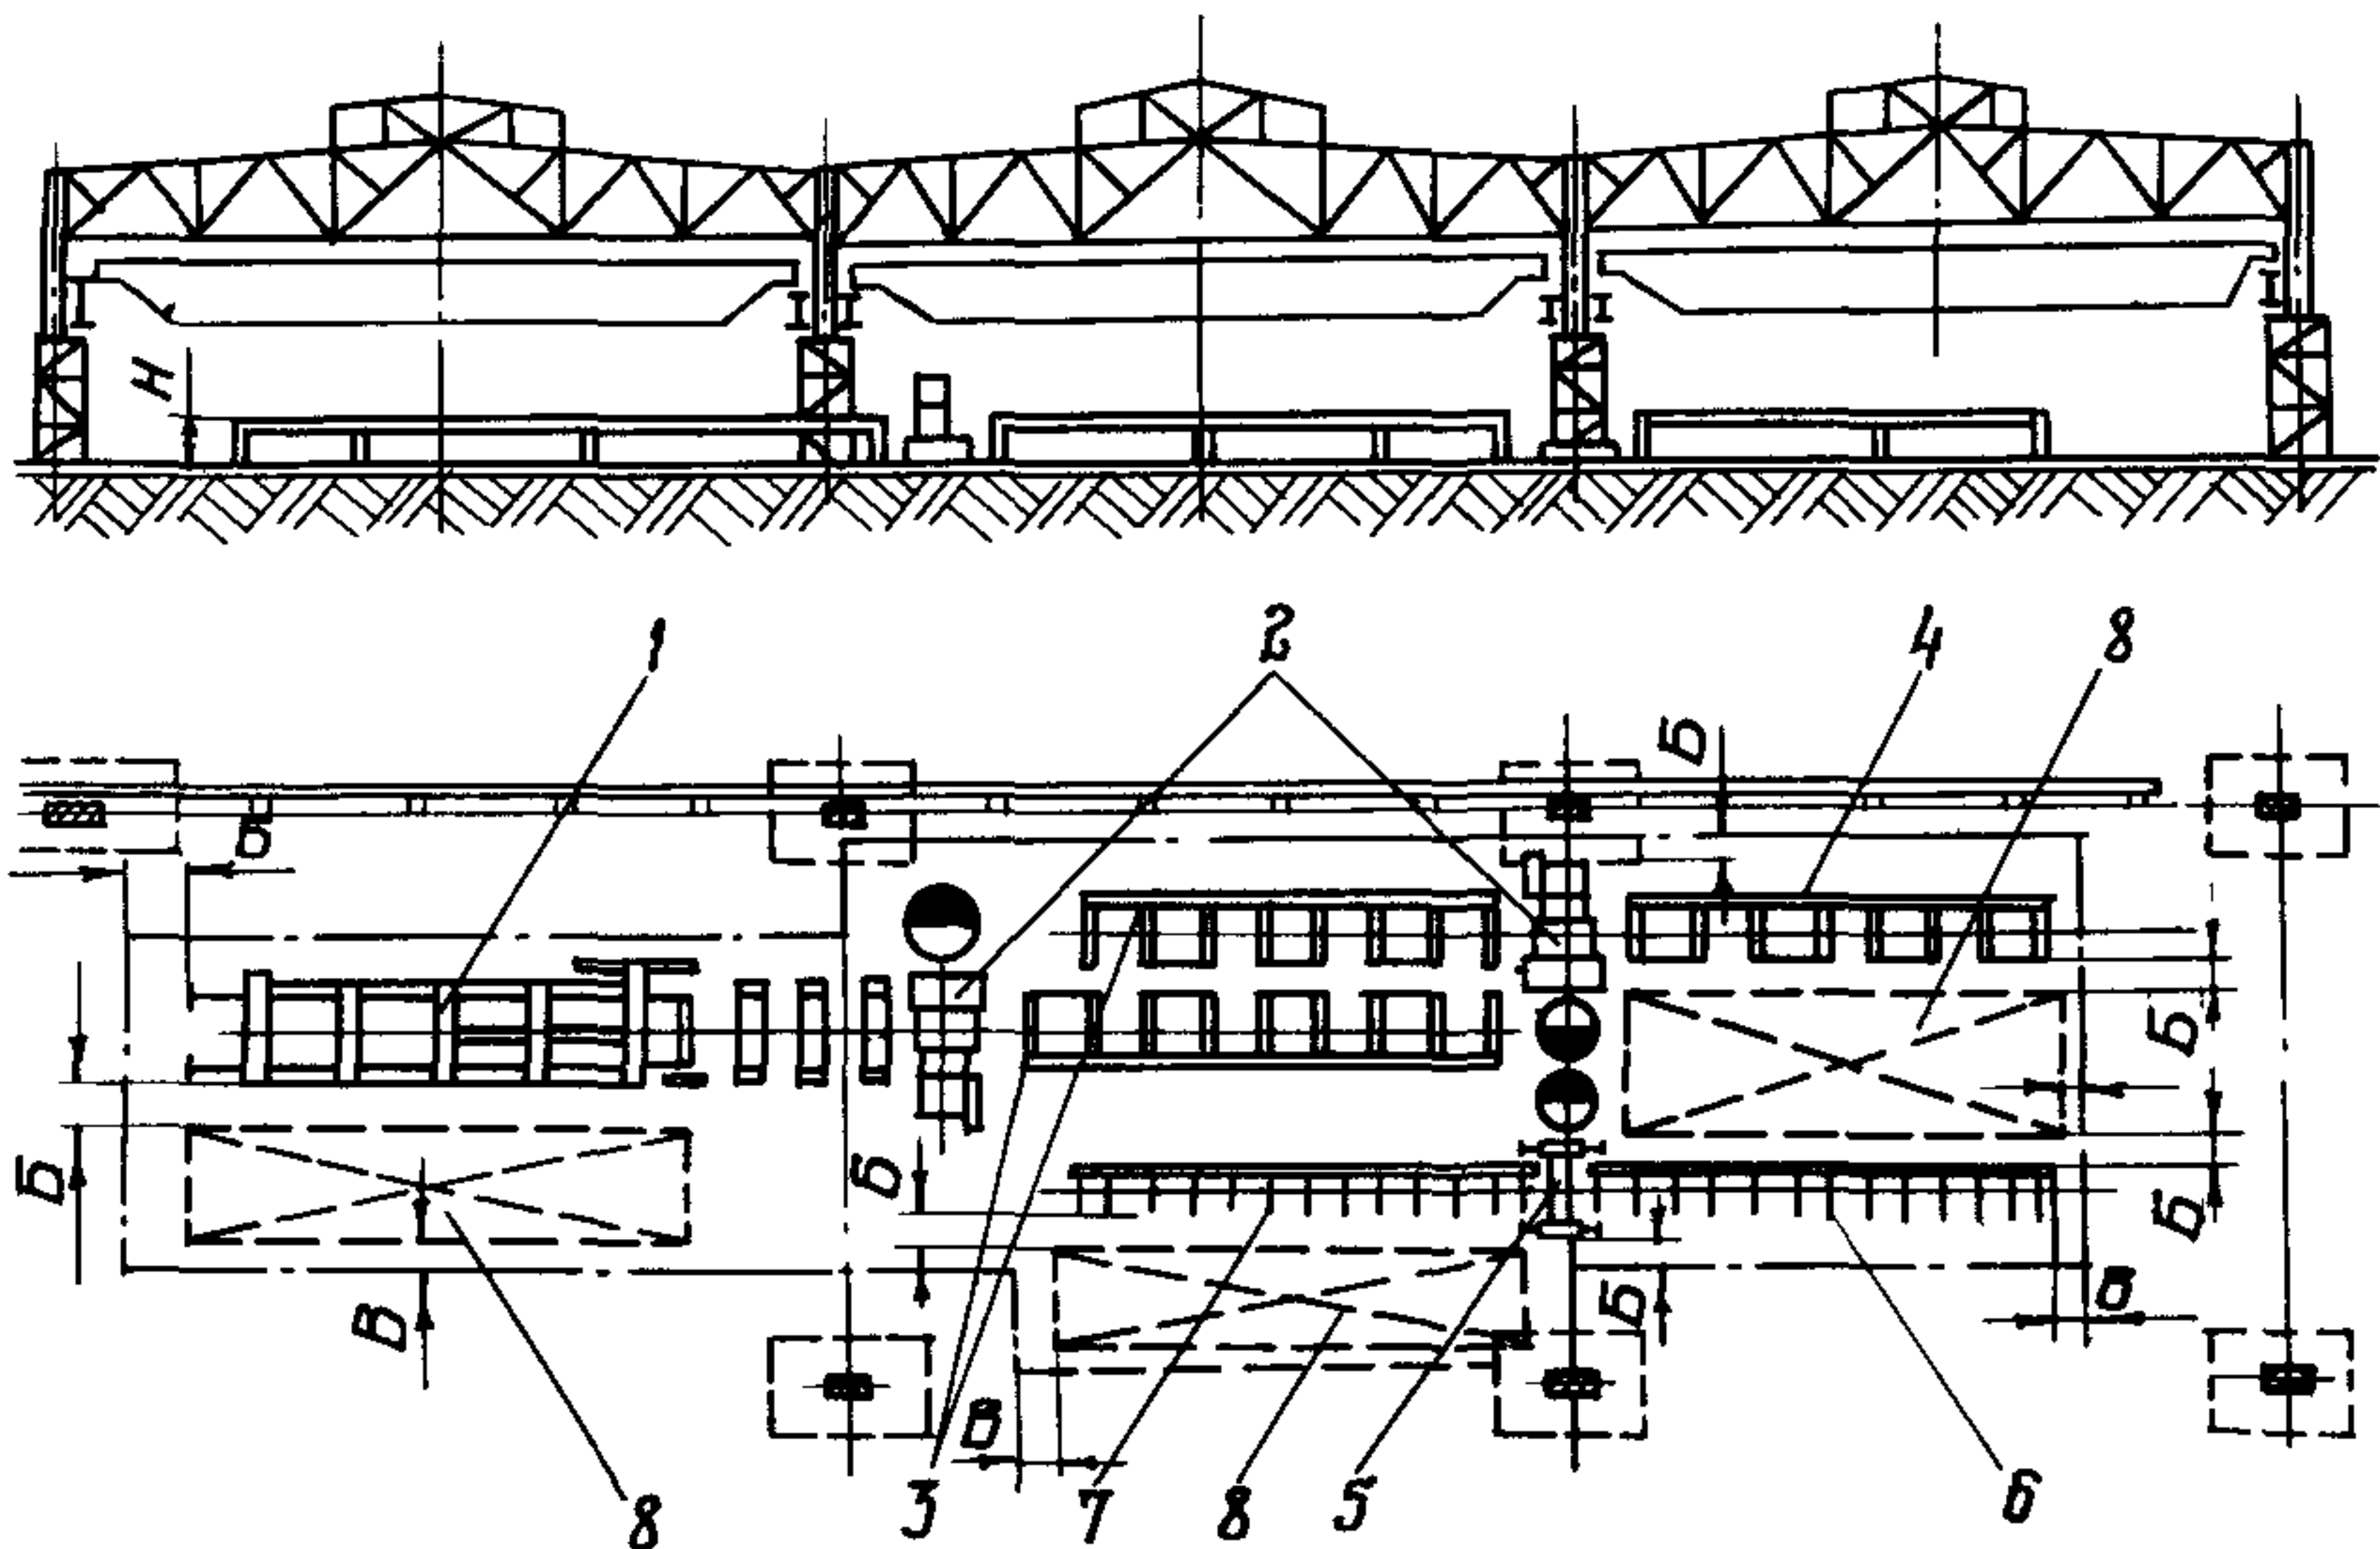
Размещение поточной линии сборки, сварки и резки стержней двутаврового сечения:
